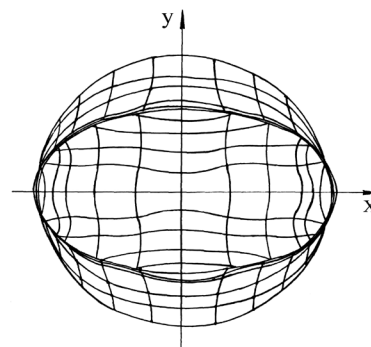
Загальний вигляд характеру переміщення металу на торцевому зрізі вальцованої заготовки
